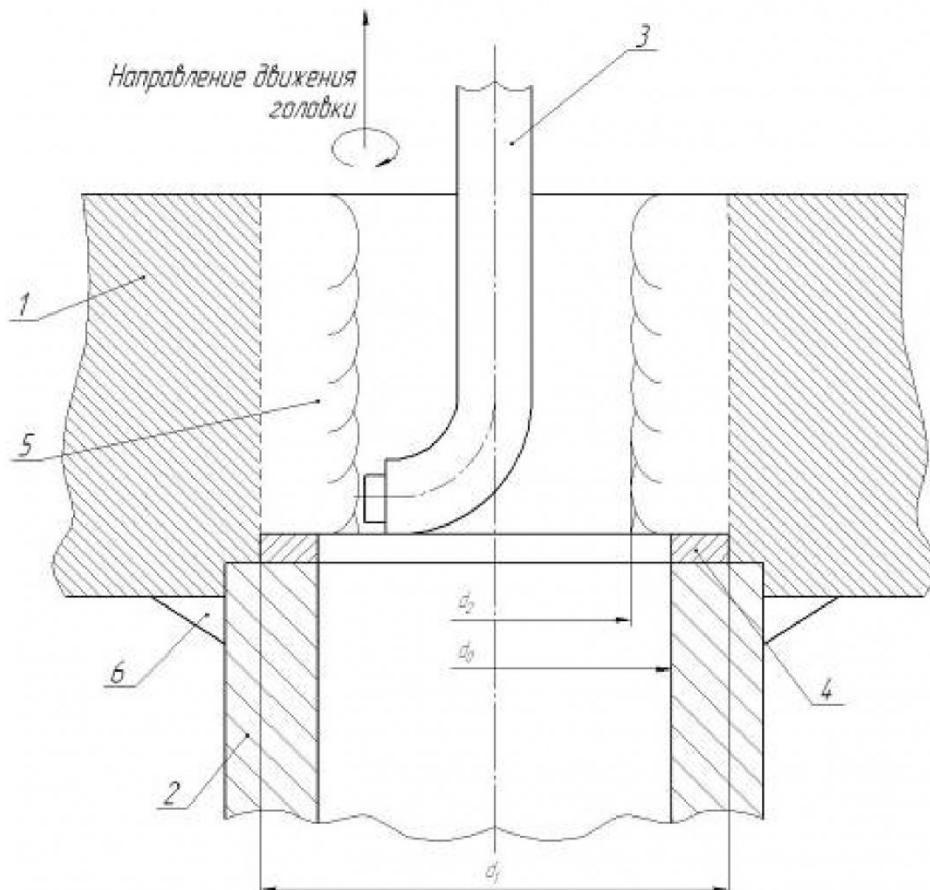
Схема восстановительной наплавки водоопускного отверстия барабана котла по технологии "Уралэнергоремонт": 1 – корпус барабана; 2 – штуцер; 3 – сварочная головка; 4 – подкладное кольцо; 5 – наплавленный металл; 6 – сварной шов.
